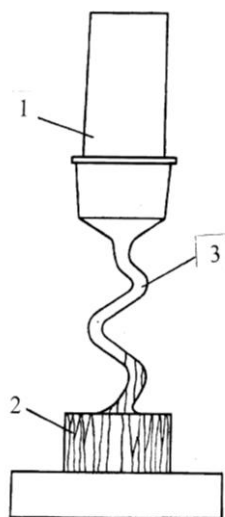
Схема устройства для получения монокристаллитных отливок
